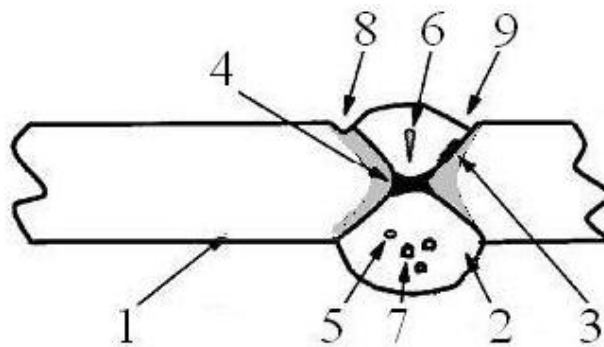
Схема зварного з'єднання з дефектами:
